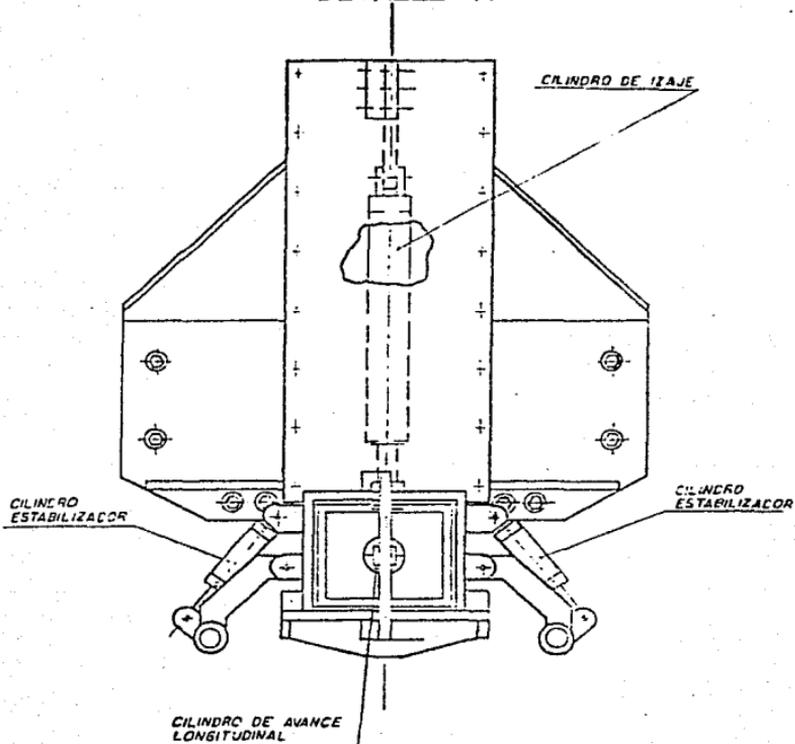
VISTA FRONTAL DEL POSICIONADOR DE DOVELAS MOSTRANDO
